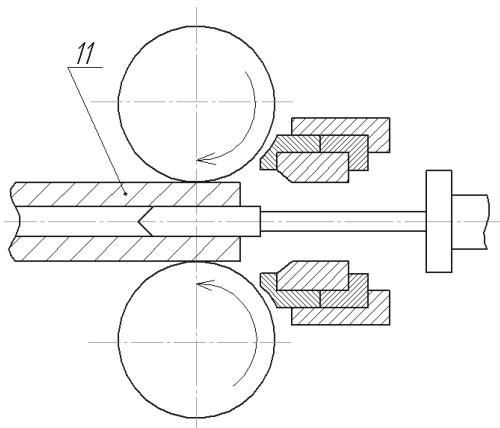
Схема устройства на стадии выпрессовки пресс-остатка: 11 – готовое изделие
